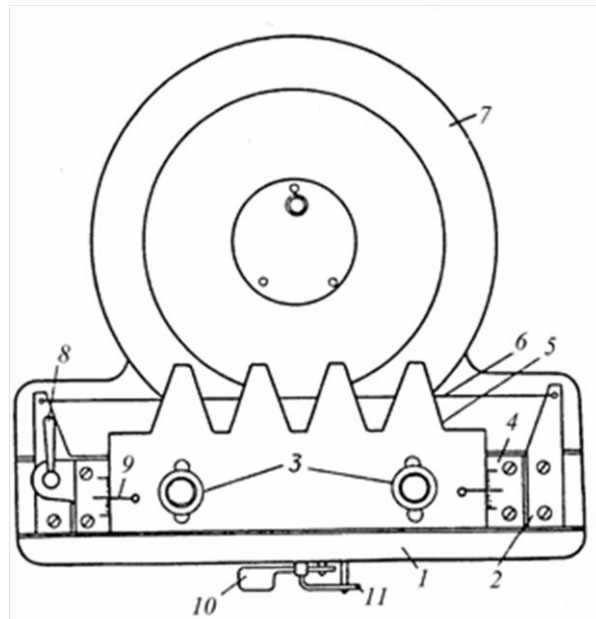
Схема лабораторної установки ТММ 42 для профілювання зубів зубчастого колеса:
